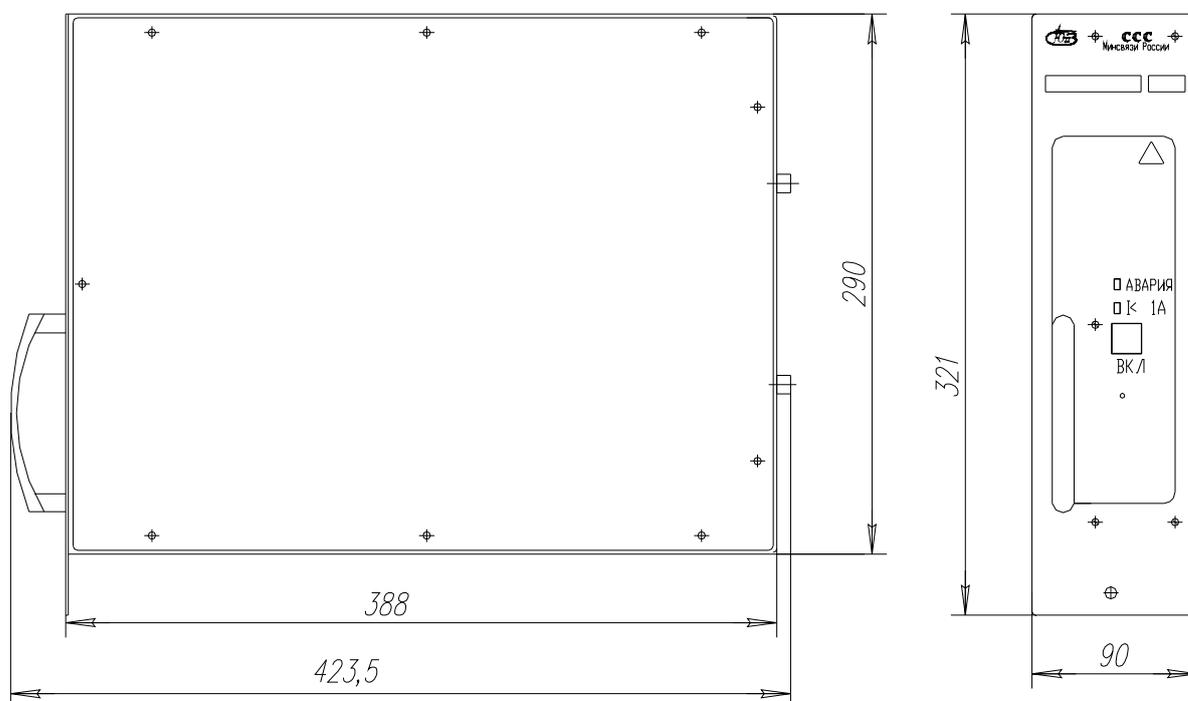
Габаритный чертеж выпрямителей ВБВ 60/60-2; ВБВ 48/65-2
